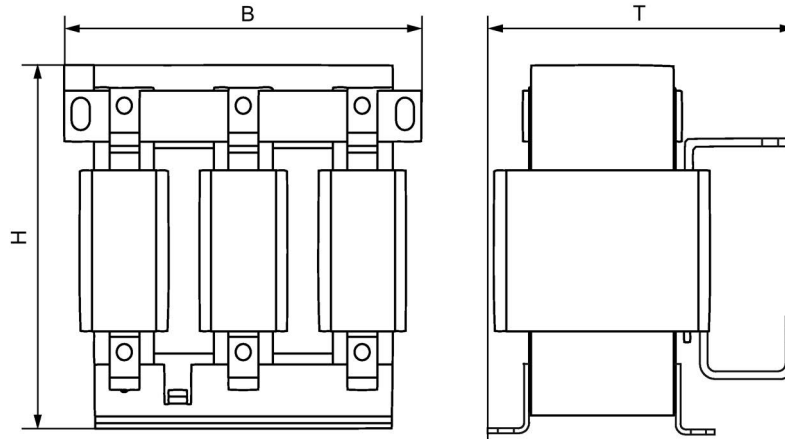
Croquis acotado bobina de motor 6SL3000-2BE35-0AA0, Typ2, para dimensiones ver tabla siguiente
